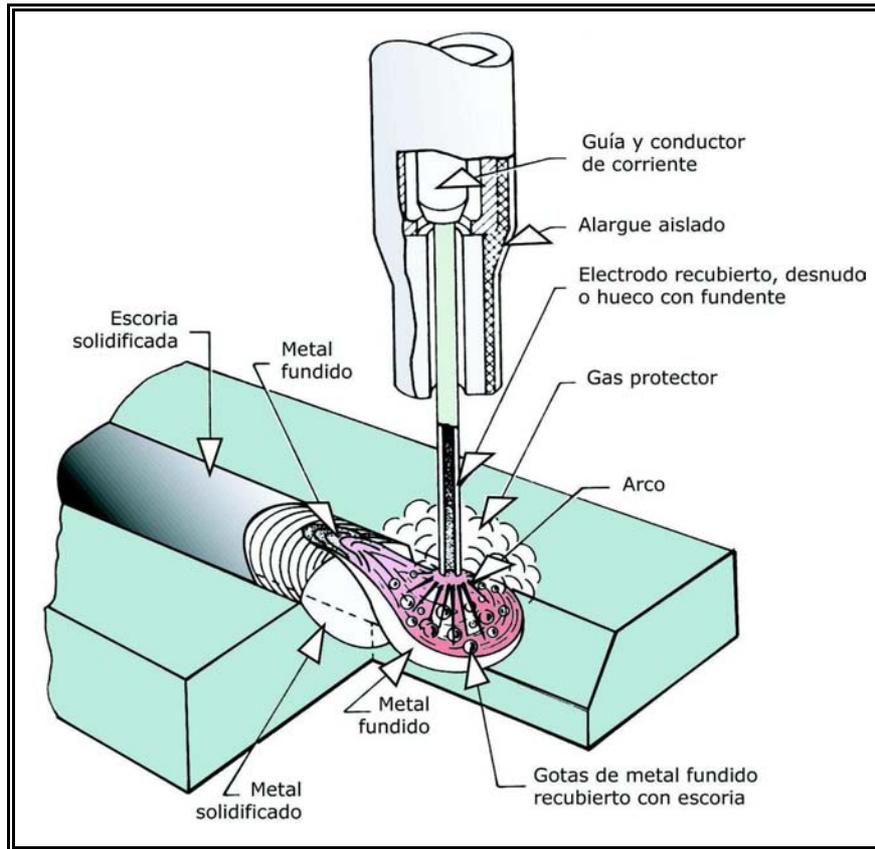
Soldadura por arco con núcleo de fundente protegida con gas.
